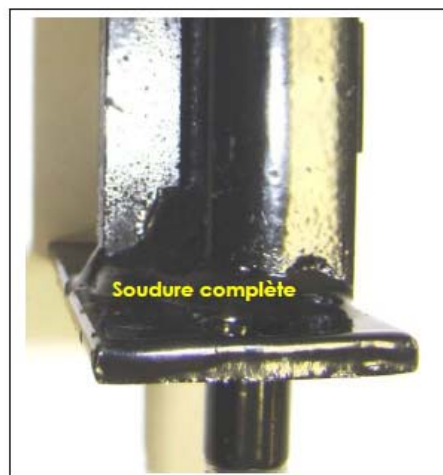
Vue latérale de la soudure complète à la base du nouveau modèle de barrure de 2014.
